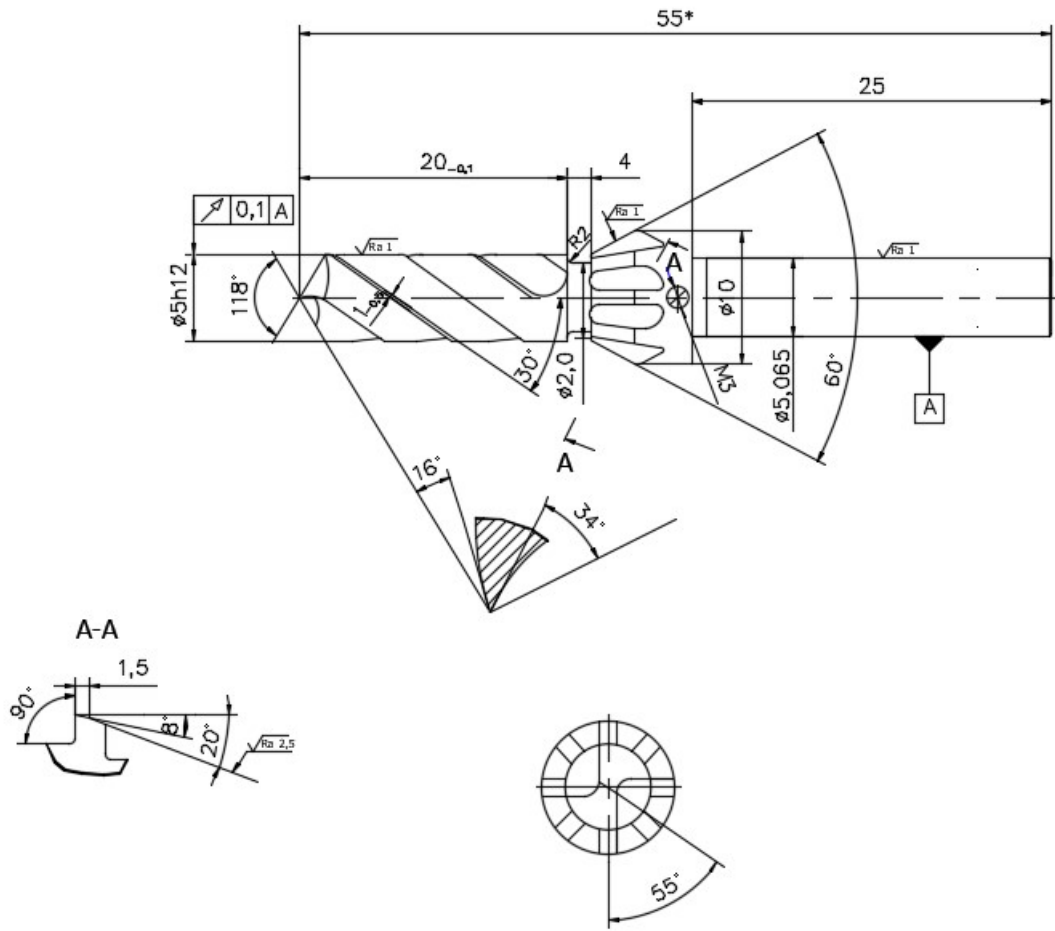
Комбінований інструмент свердло-зенківка
